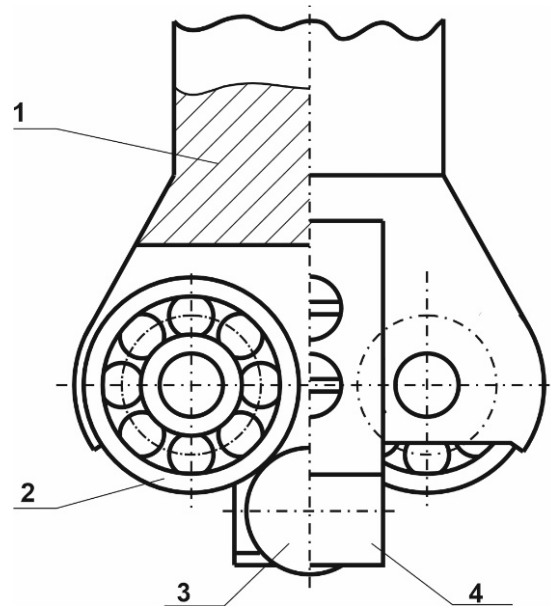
Робоча частина кулькового вигладжувача: 1 – шток; 2 – підшипники для утримання кульки та створення натягу; 3 – вигладжувальна кулька; 4 – запобігач від випадання кульки
